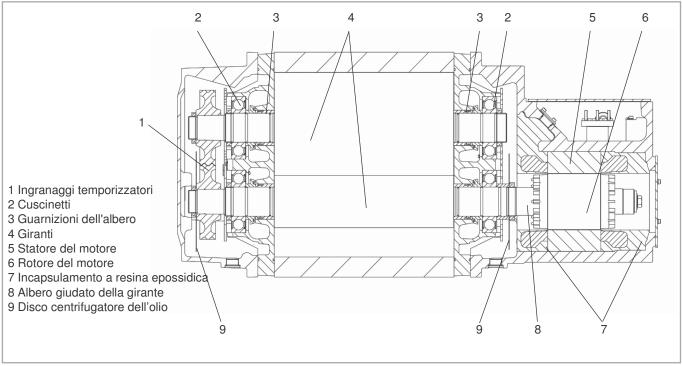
Sezione longitudinale di una RUVAC WH 4400 (flusso orizzontale)
